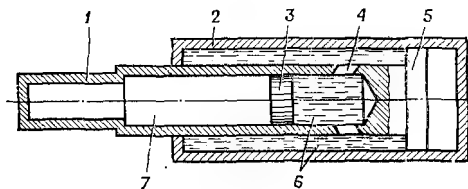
Схема гидропневматического накатника с плавающим поршнем: 1 — шток; 2 — цилиндр; 3 — плавающий поршень; 4 — соединительные отверстия; 5 — поршень; 6 — жидкость; 7 — газ.
